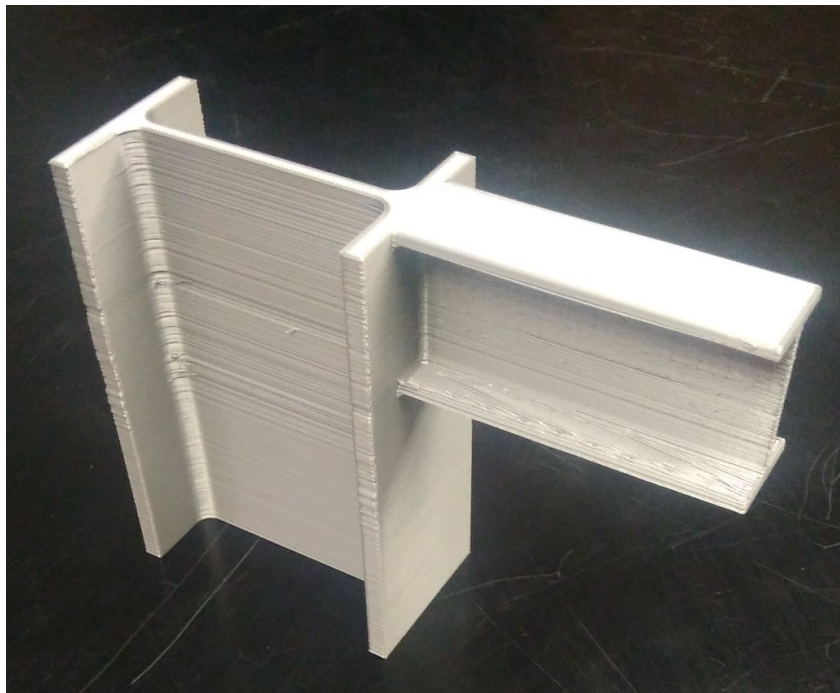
Pieza de uniones soldadas impresa en PLA
